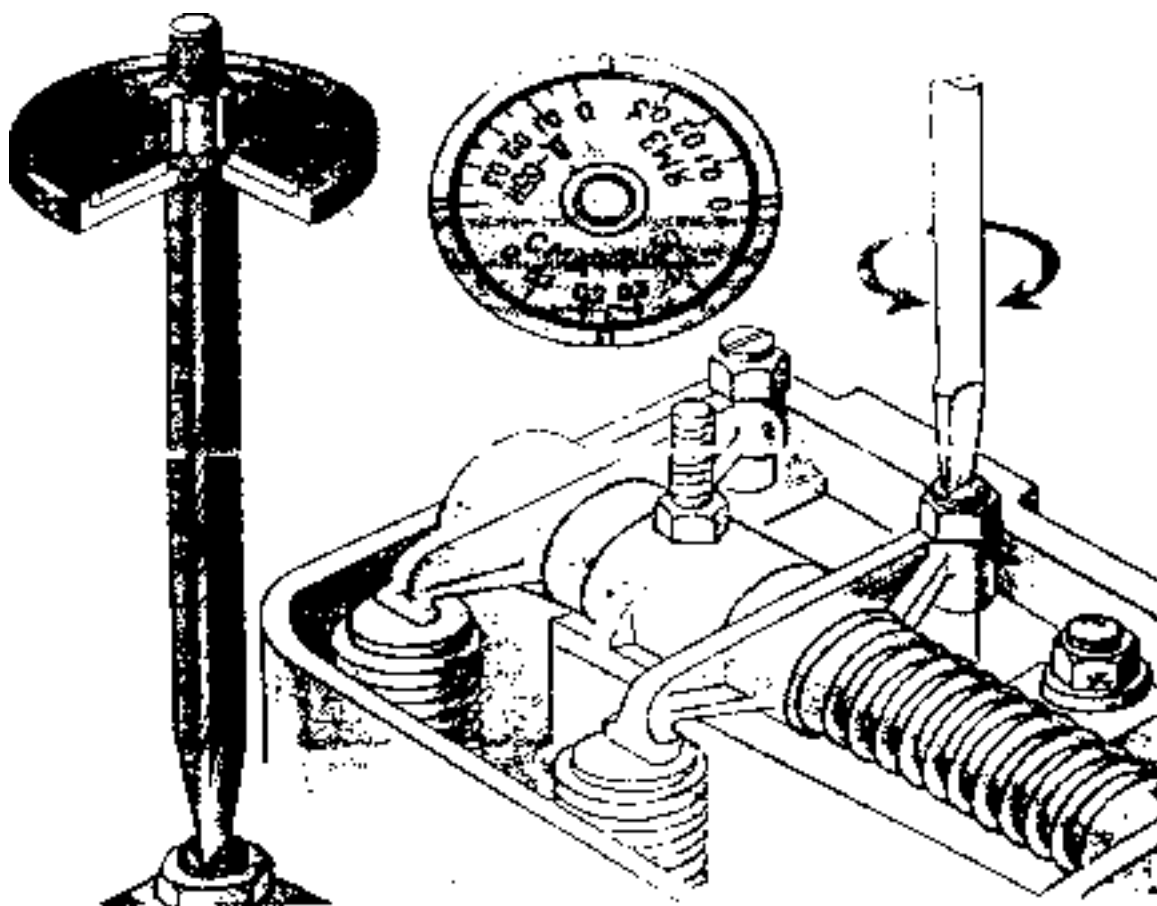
Приспособление ПИМ - 5226 ГОСНИТИ для регулировки зазоров клапанов двигателей
